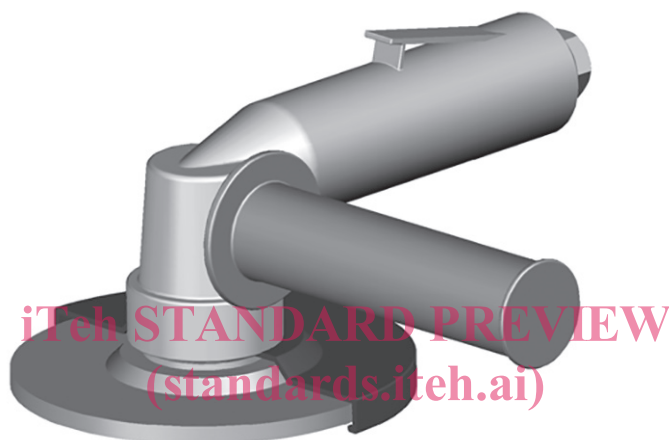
Meuleuse d'angle pneumatique où le moteur sert de poignée principale
